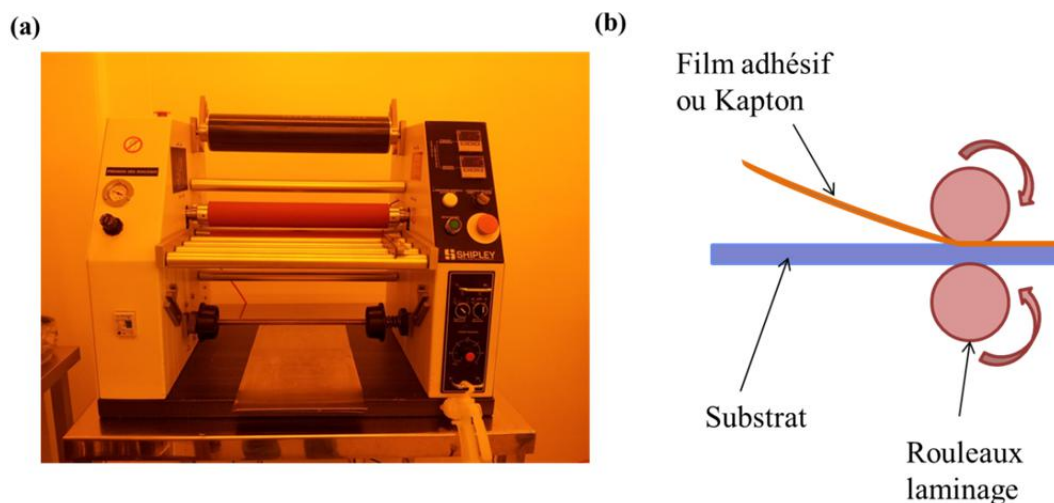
Photo (a) de la machine de laminage Shipley 360 et schéma de principe (b) du laminage.
